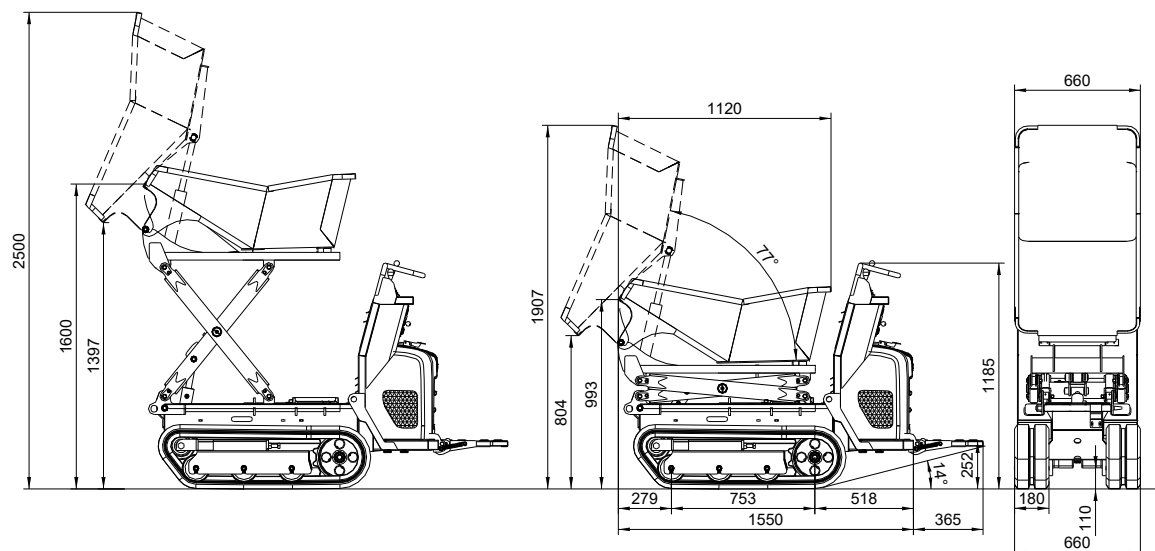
Køretøjets dimensioner (type DT05-D med løftbart tippelad)
